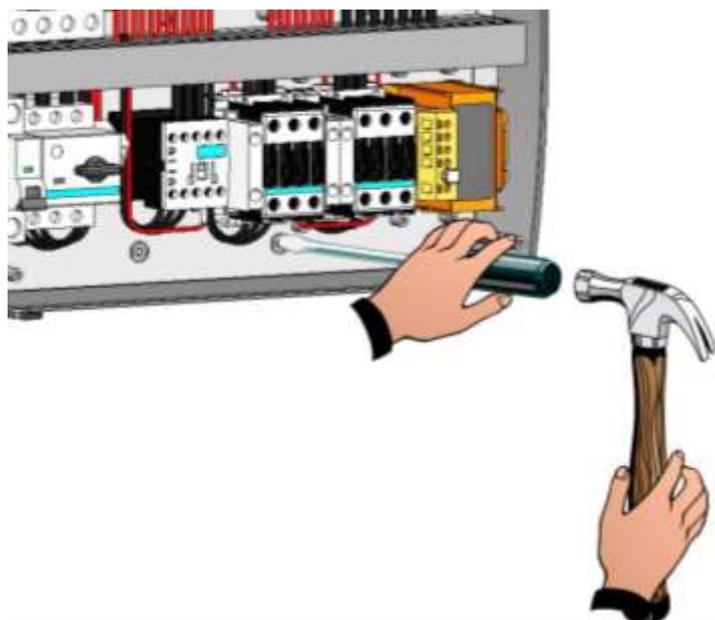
Per mezzo di un cacciavite premere sui quattro fori preimprontati del fondo per realizzare le forature di fissaggio del quadro elettrico.
